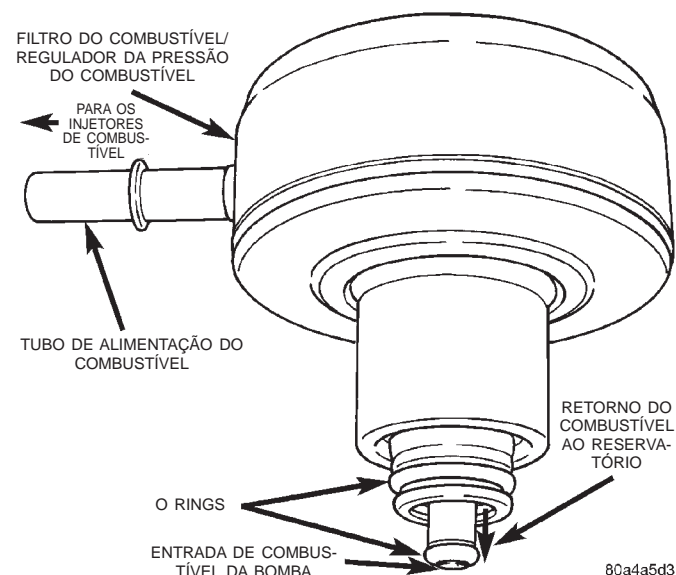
Filtro do Combustível/Regulador da Pressão do Combustível
